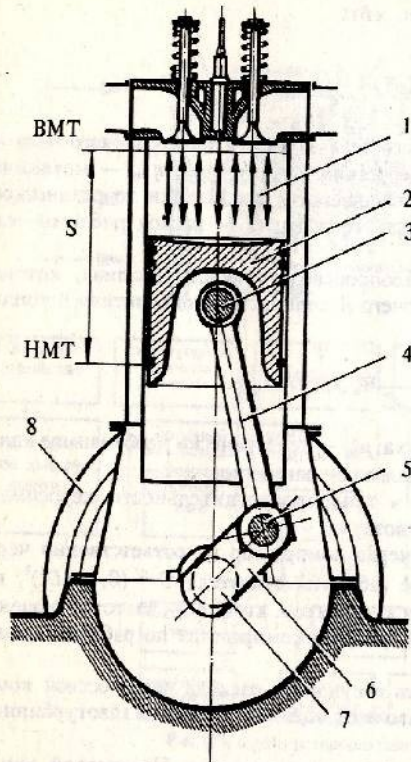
Схема поршневого двигателя: 1 — цилиндр; 2 — поршень; 3 — поршневой палец для шарнирного соединения поршня с шатуном; 4 — шатун; 5 — шейка кривошипа коленчатого вала; 6 — кривошип коленчатого вала; 7 — коленчатый вал; 8 — маховик
